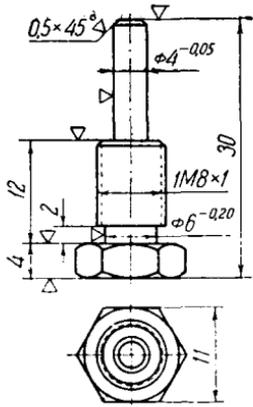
Дет. № 16-11. Ось рычага поплавка для керосина
